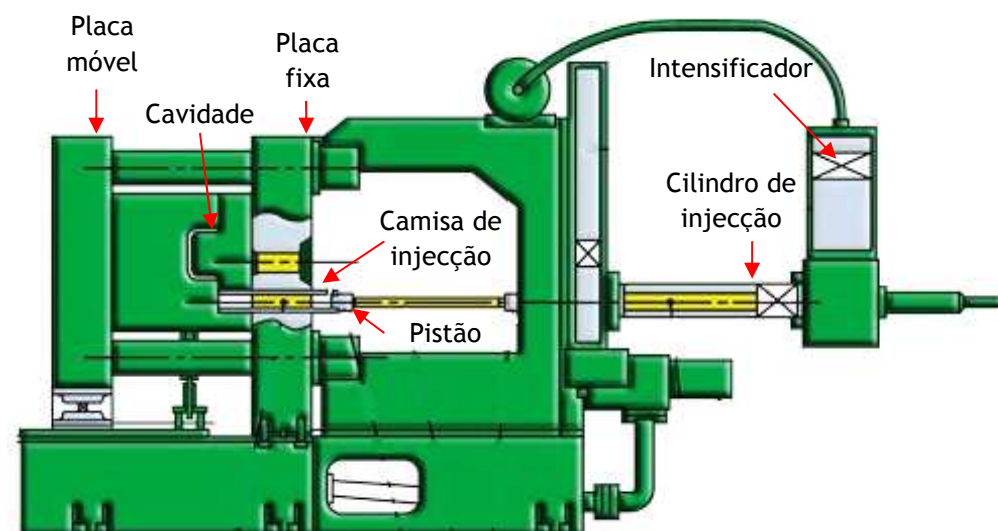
Equipamento de fundição injectada em câmara fria [6]
